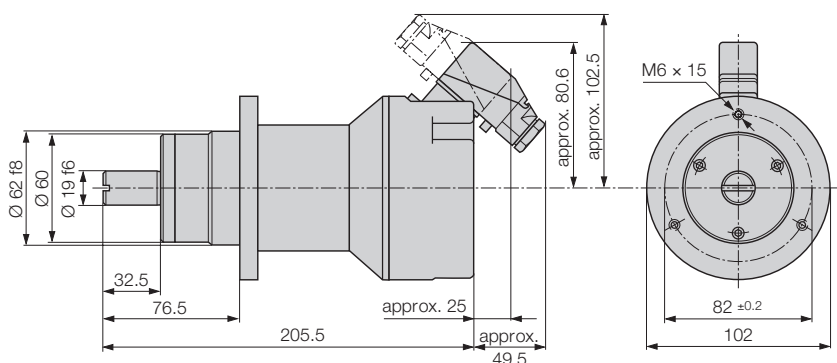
KINAX WT 707 с дополнительным редуктором и штекером.
